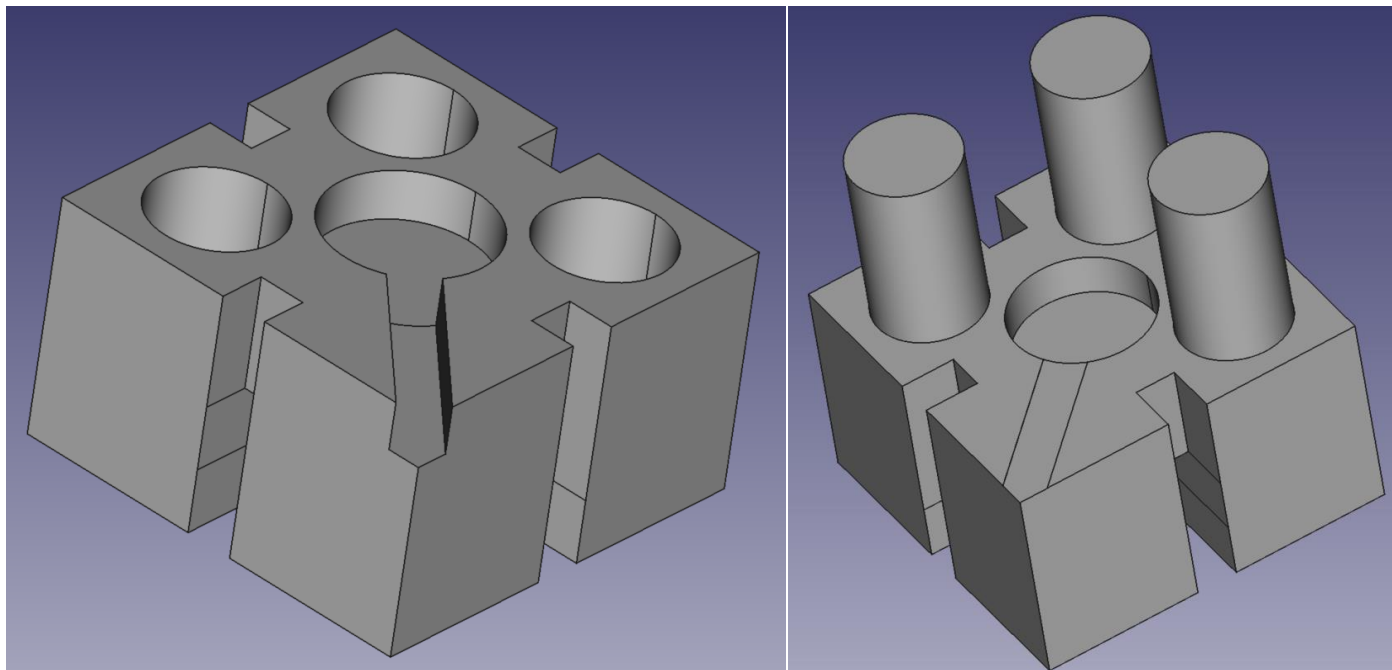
Dessin 3D des deux pièces du support de bobine. Dessiné sous FreeCAD.
